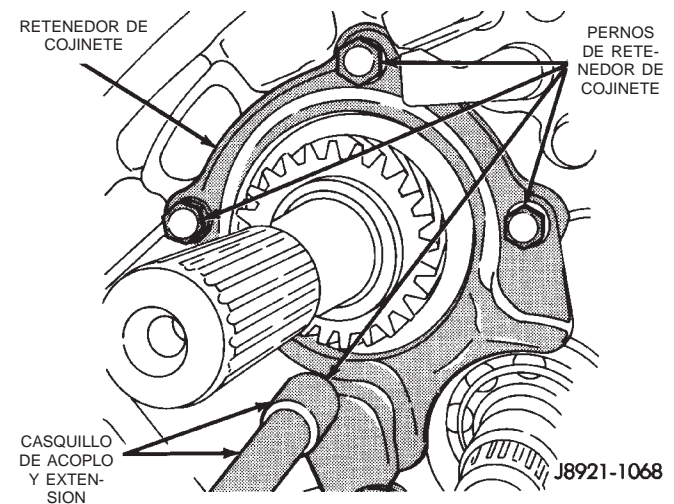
Desmontaje de pernos de retenedor del cojinete trasero del eje transmisor
